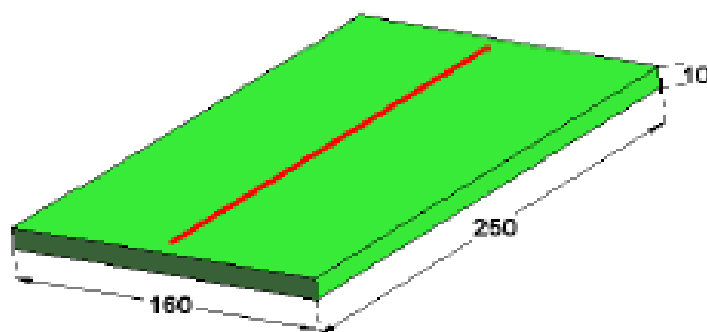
Géométrie de la plaque soudée en (mm).
